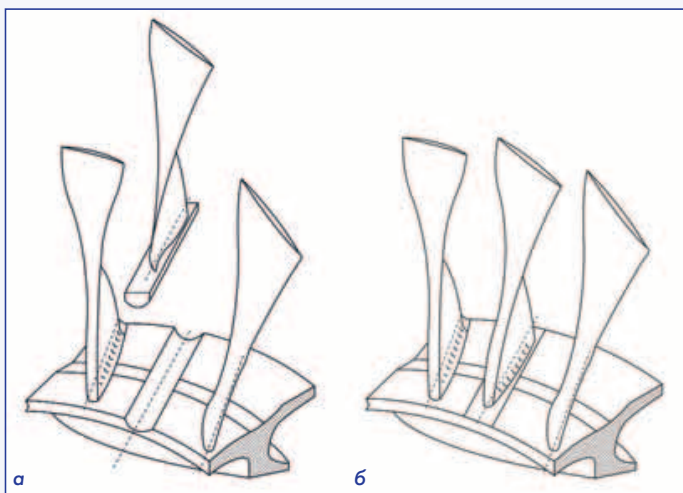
Способ ремонта моноколес сваркой трением:
